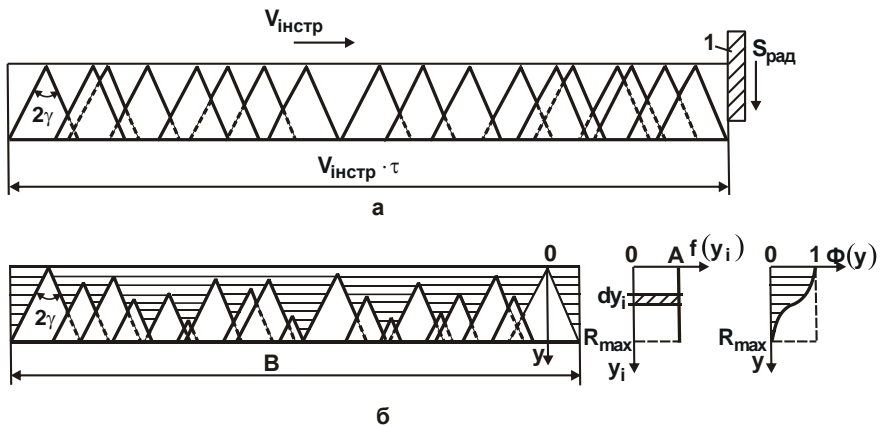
Схема накладення проєкцій зерен на площину оброблюваного зразка (а) і загальний вигляд шорсткуватої шару оброблюваної поверхні (б): 1 – оброблюваний зразок
